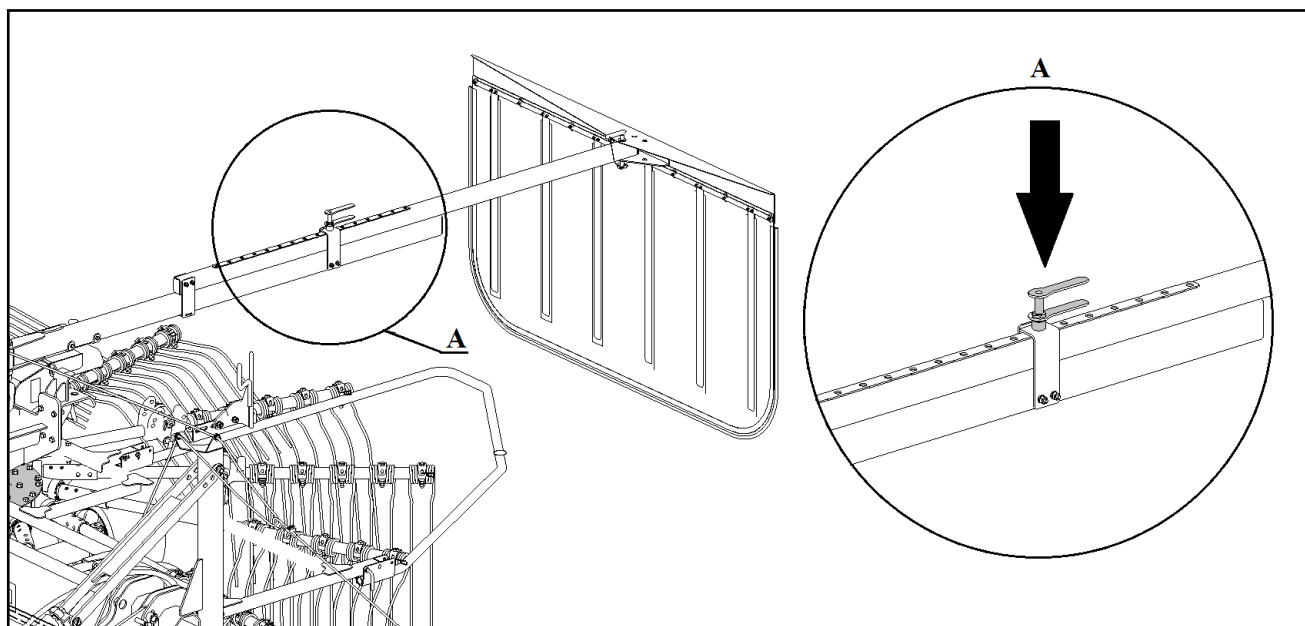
Стопорный винт регулировки ширины валка
